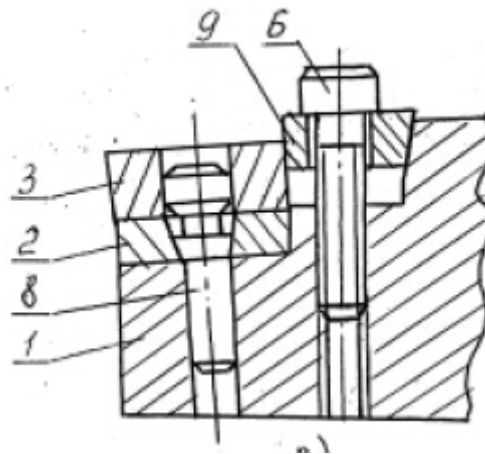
Схема кріплення пластинок клиновою планкою
